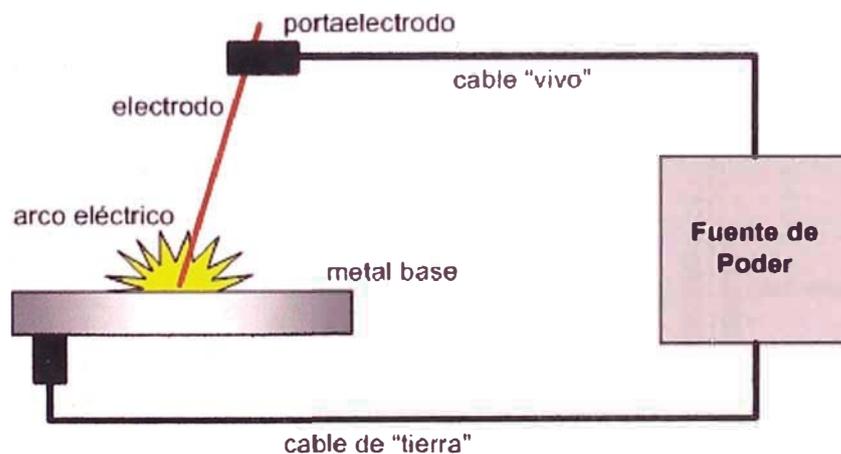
Circuito de soldadura por arco eléctrico
